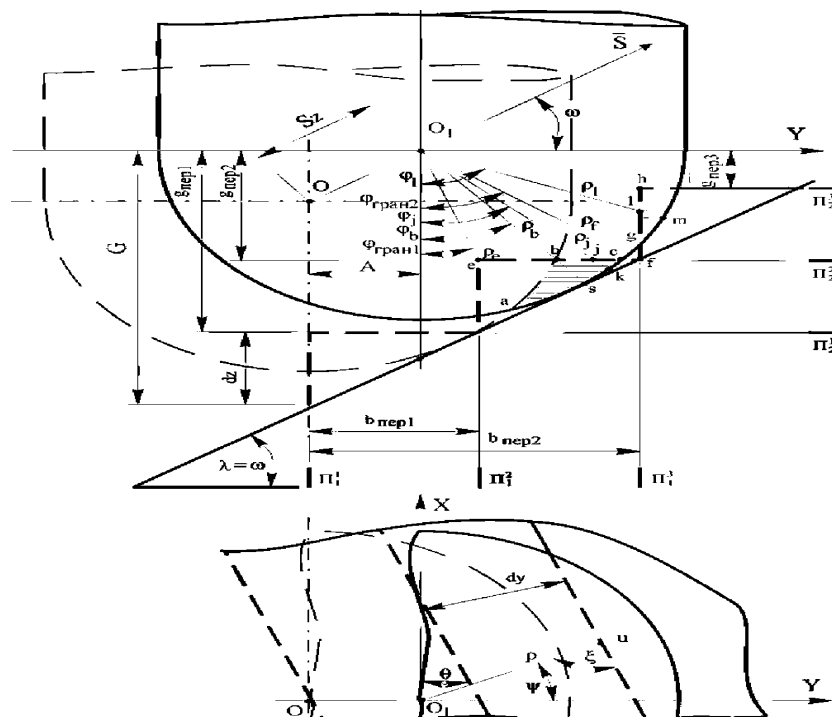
Розрахункова схема для визначення товщини шару, що зрізується при фрезеруванні просторово-складної поверхні
